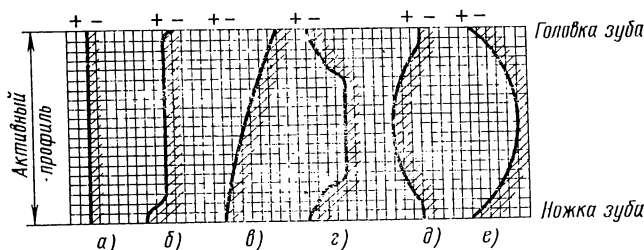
Типовые модифицированные формы профиля зубьев шевера
